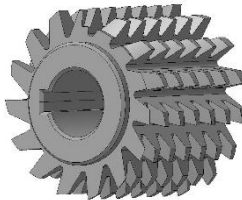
3-Д модель деталі фрези черв'ячна
